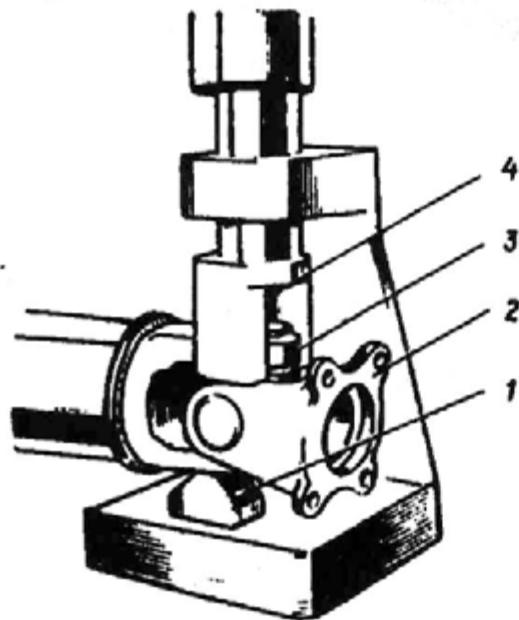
Выпрессовка корпуса подшипника карданного шарнира с помощью приспособления:
